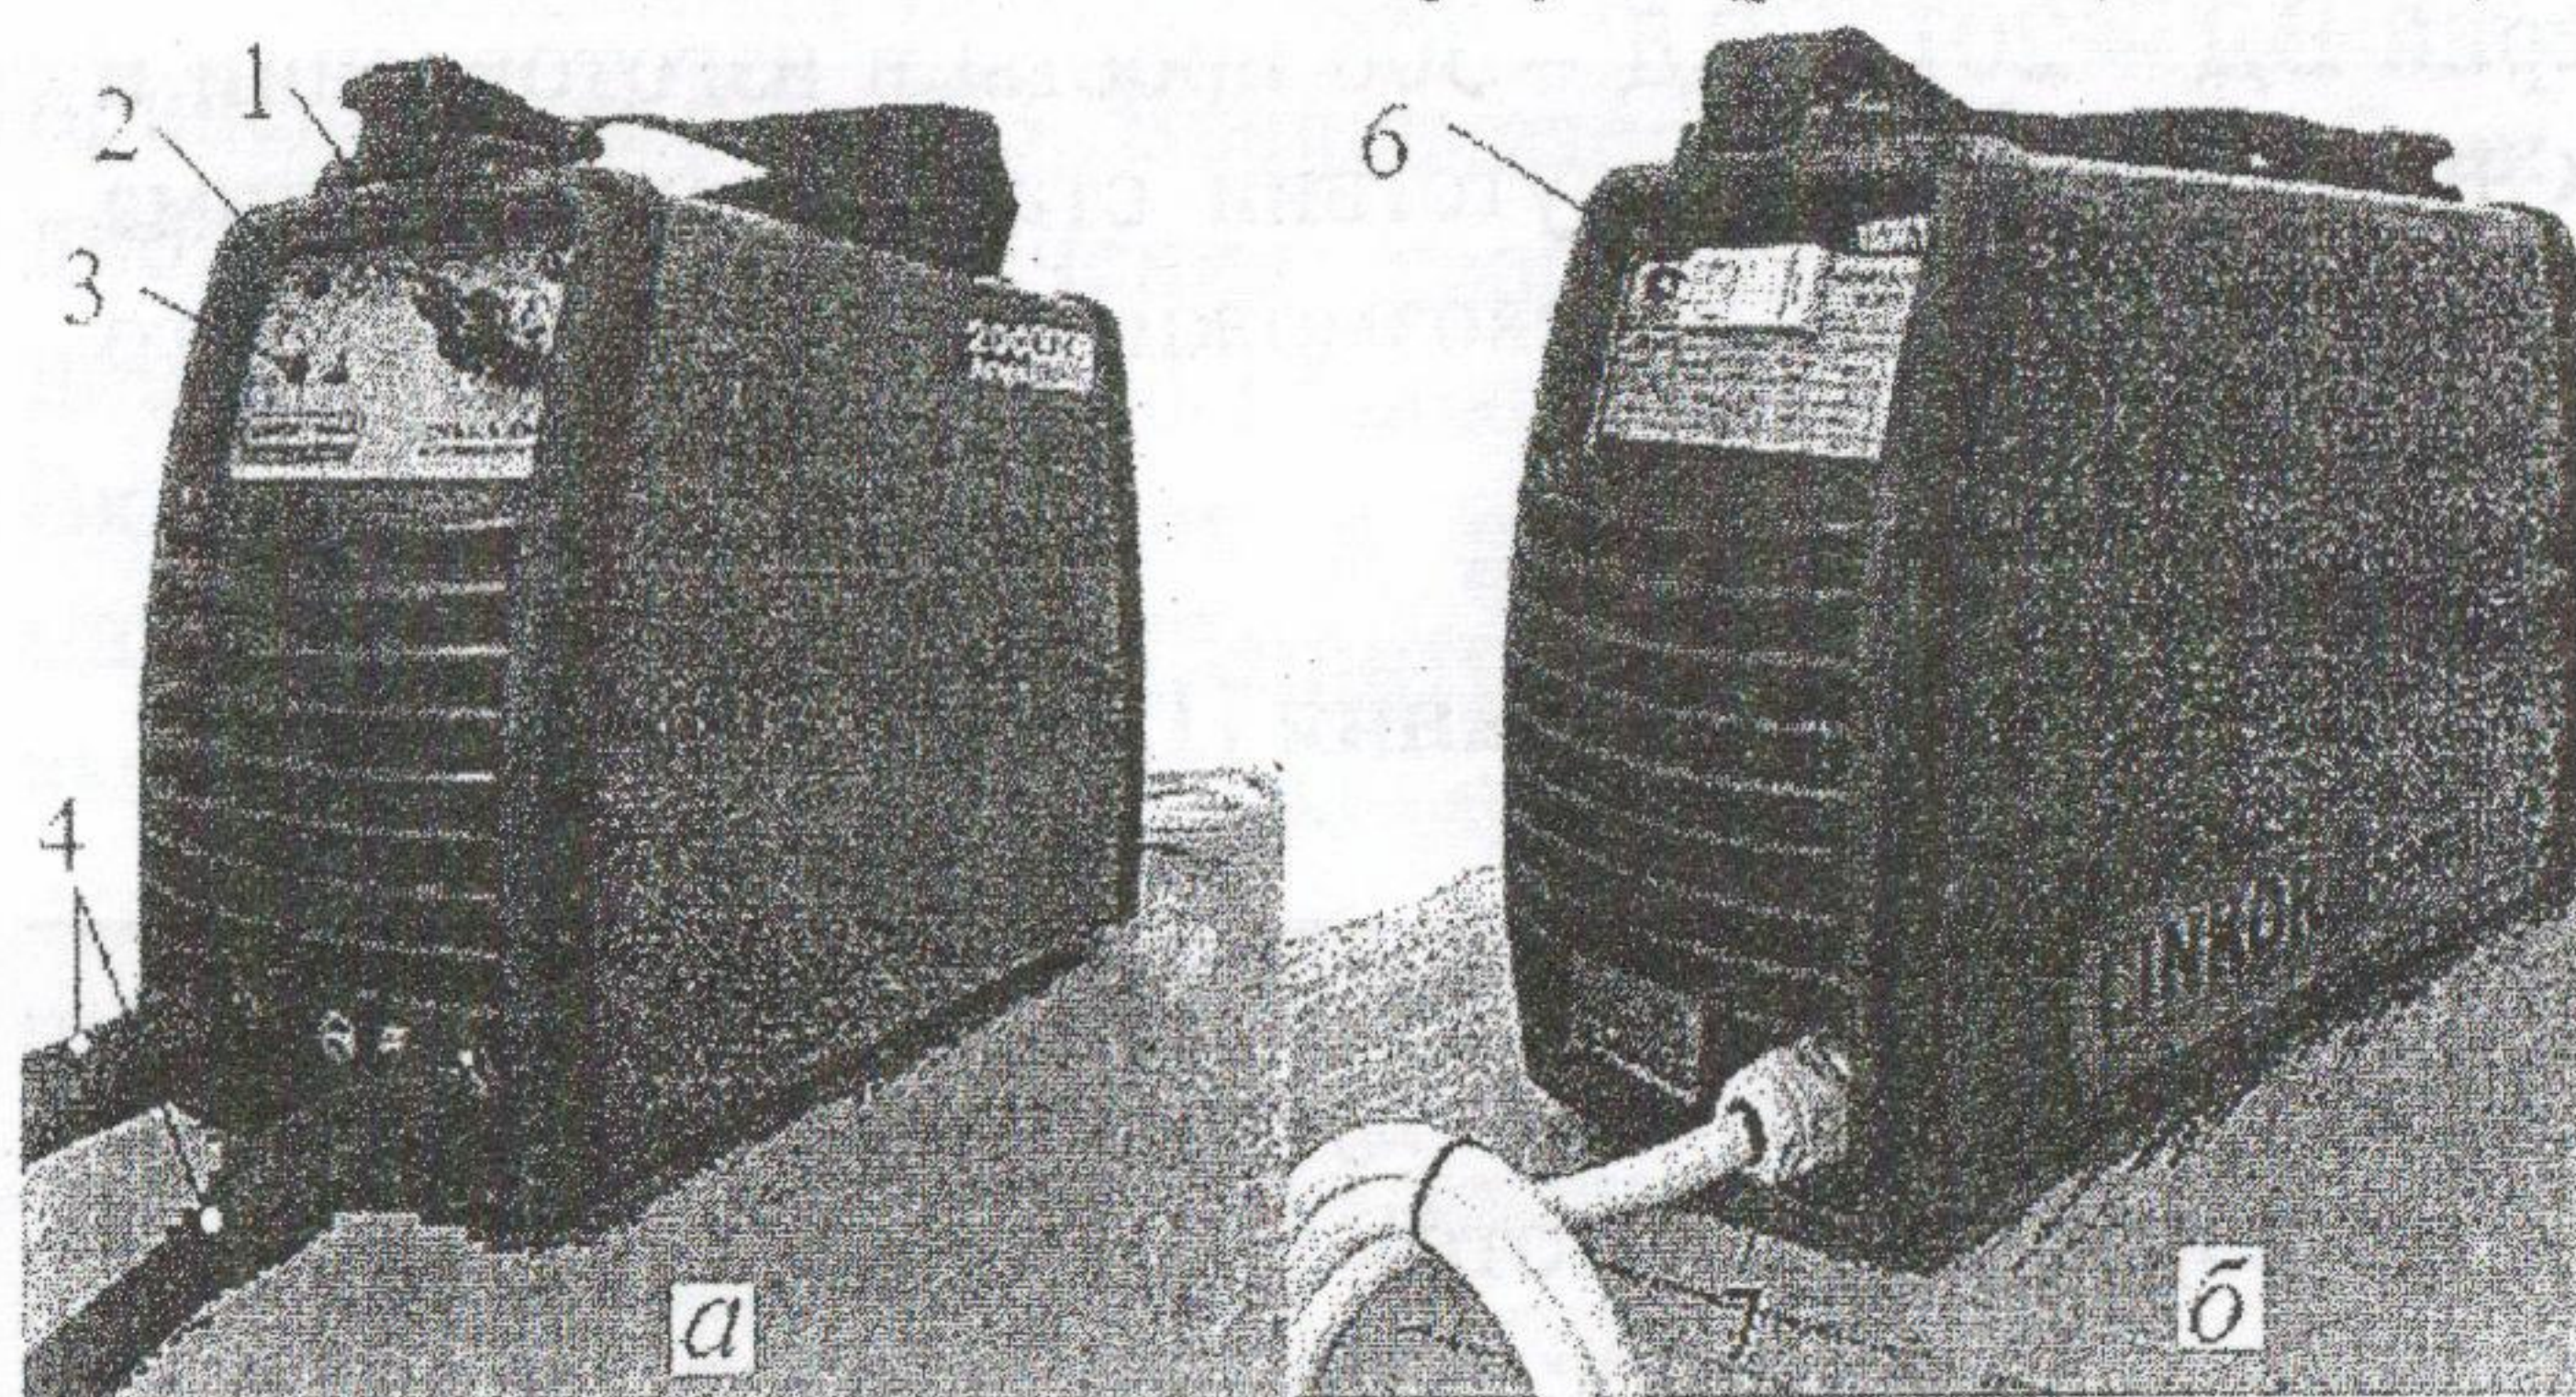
Внешний вид инверторного сварочного аппарата:
